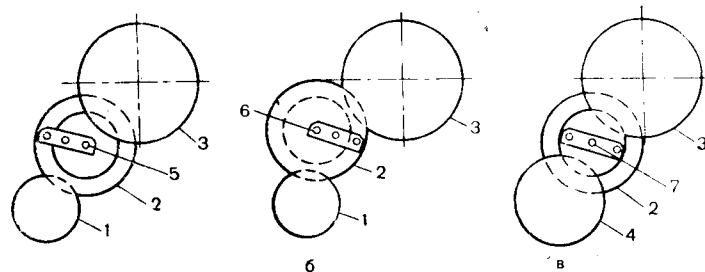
Установка шестерен механизма передачи на высевające аппараты сеялки СОН-2,8.
